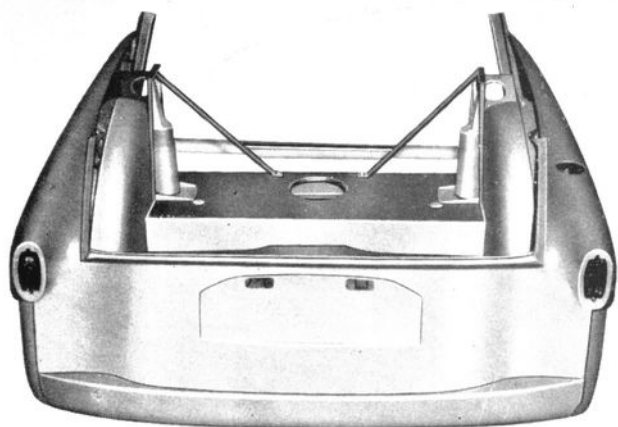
Úplný zadní blatník pravý, s podběhy.
